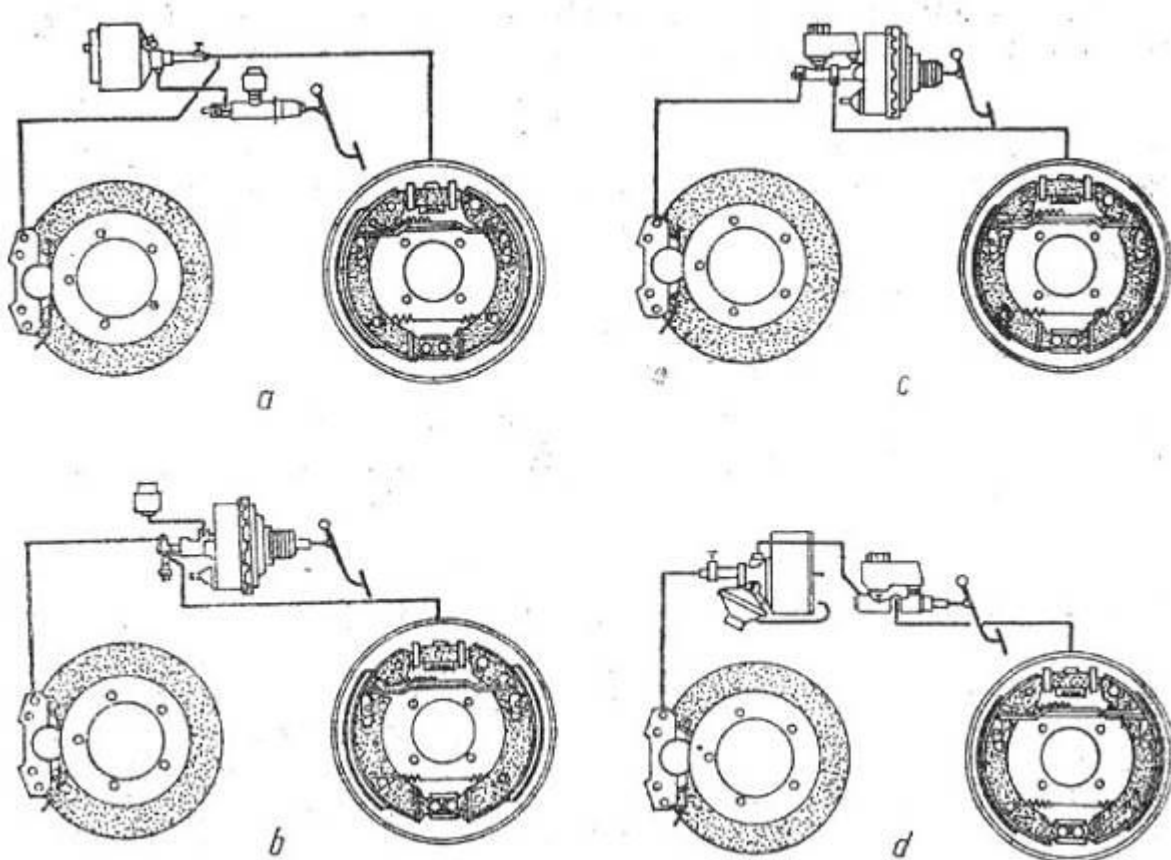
Tipuri de dispozitive de frinare cu transmisie hidraulică, cu servomecanism vacuumatic.
